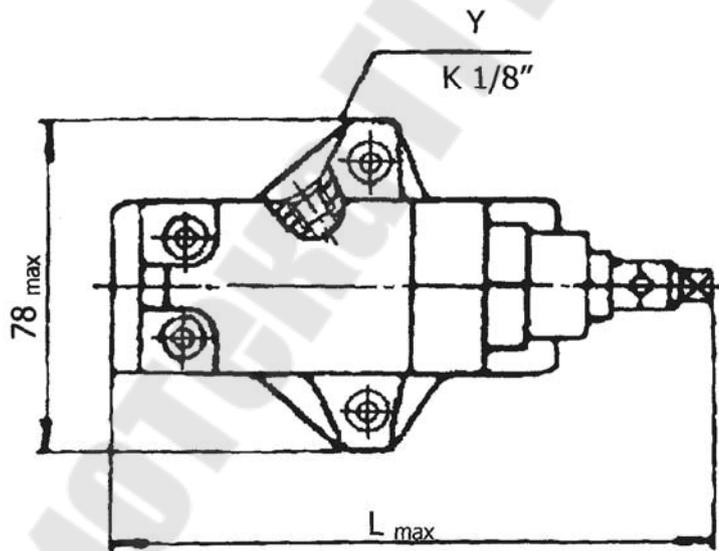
Общий вид и присоединительные размеры клапанов редукционных МКРВ - */3Т
